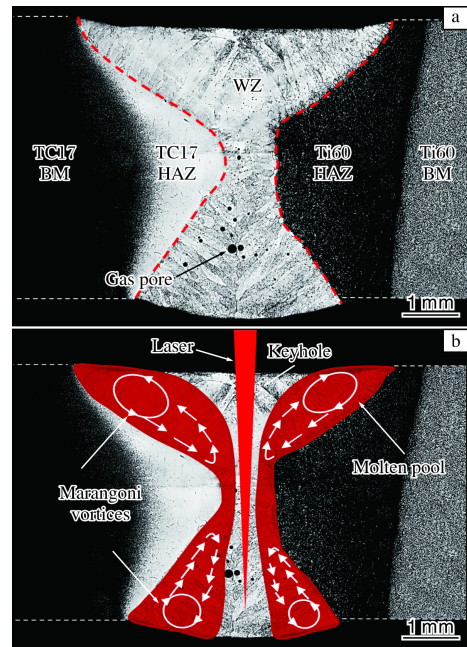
TC17/Ti60 合金激光焊接接头横截面的宏观形貌及 X 型焊缝形成原理示意图
